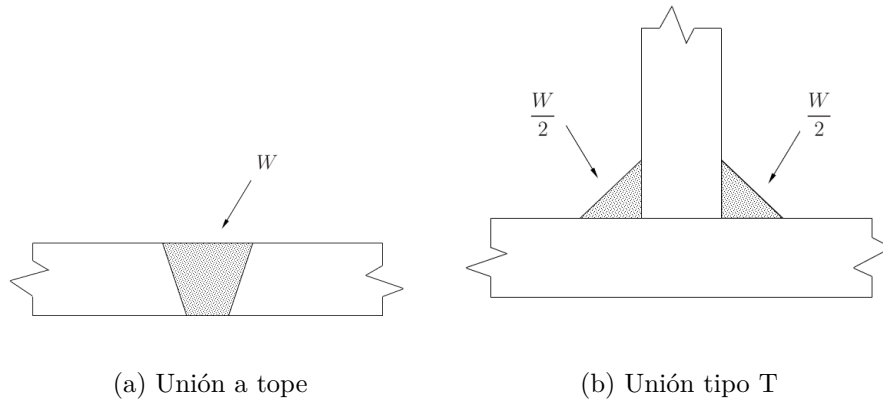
Metal de soldadura depositado en dos uniones. [7]
